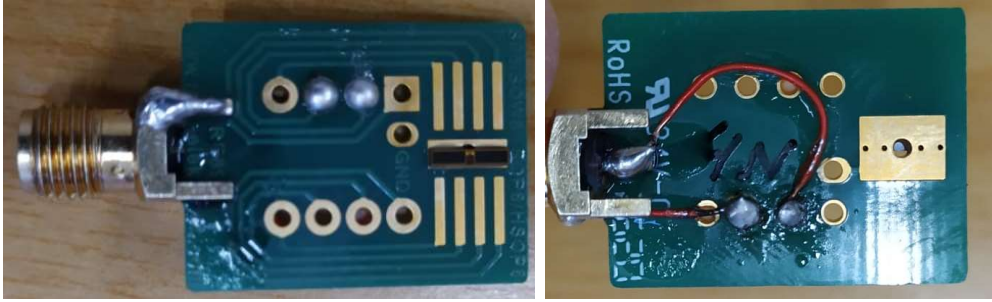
Conector SMA soldado a la PCB sobre la que se encuentra la rectena.
